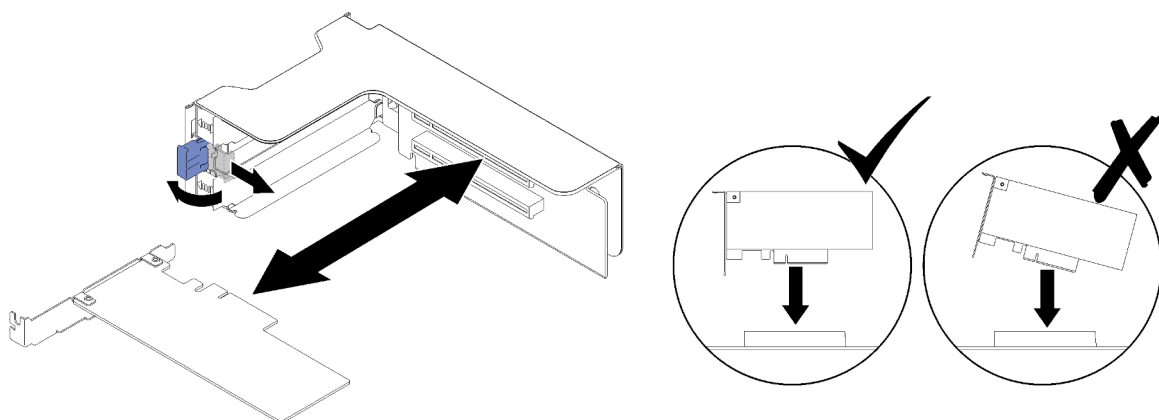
Remoção do adaptador da Conjunto da placa riser PCIe
